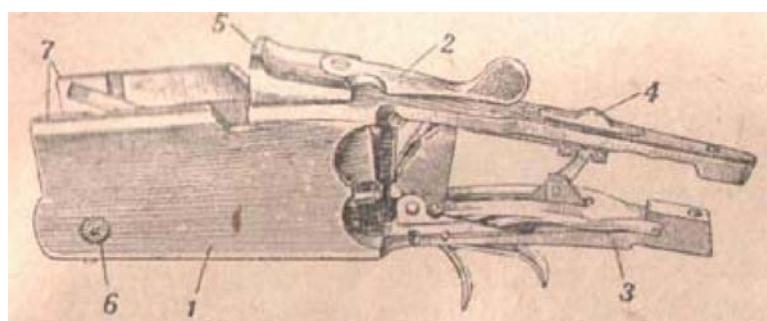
колодка двуствольного дробового ружья с вертикально спаренными стволами, модель МЦ-6: 1 - корпус коробки; 2 - ключ затвора; 3 - нижняя личина со спусковым и ударным механизмами; 4 - кнопка переключения предохранителя; 5 - щиток коробки; 6 - ось шарнирной муфты; 7 - боковые стенки коробки (щечки)
